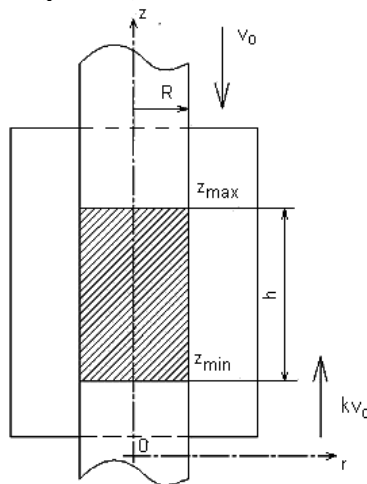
Схема ущільнення циліндричної заготовки у закритому штампі
